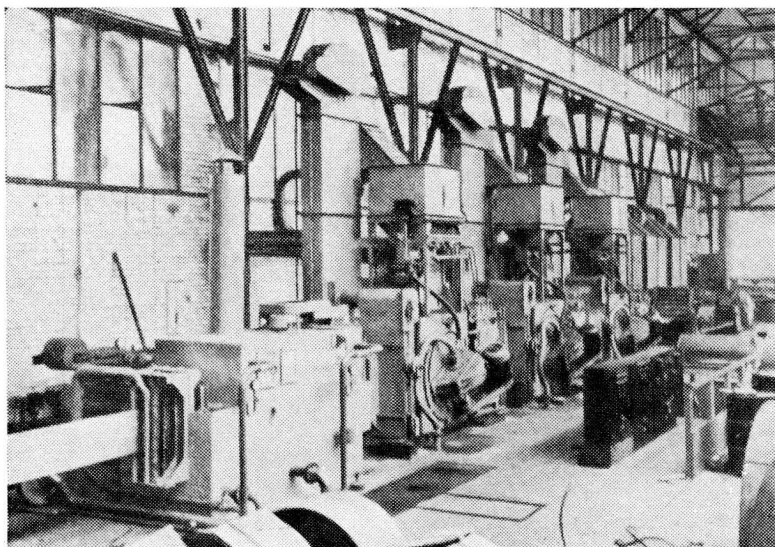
Máquina para decapagem mecânica por jato de areia com transporte mecânico com fita de aço; 6 aparelhos de limpeza centrífuga com adicional equipamento de lavagem (A. Gutman Ag., Hamburgo).
